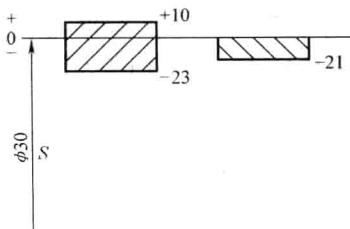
过渡配合尺寸公差带图（偏差单位为 μm ）
